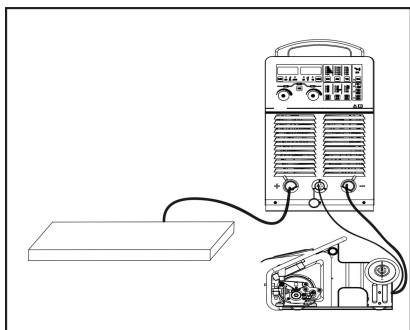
Instalación de cables de soldadura
